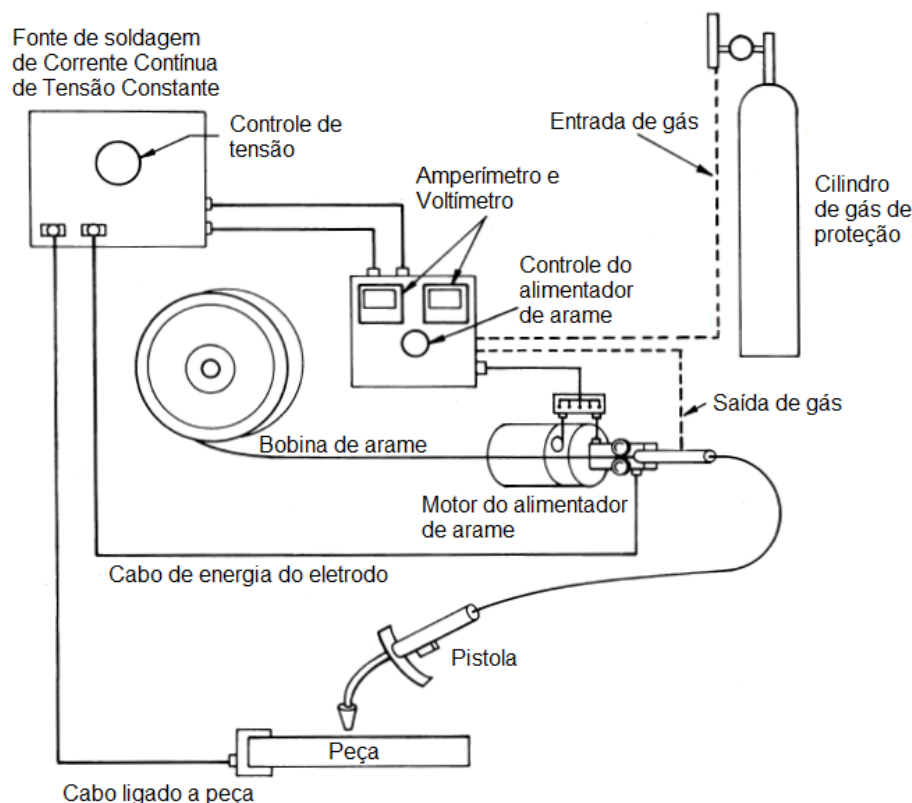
Esquema do equipamento de soldagem AT [16].
